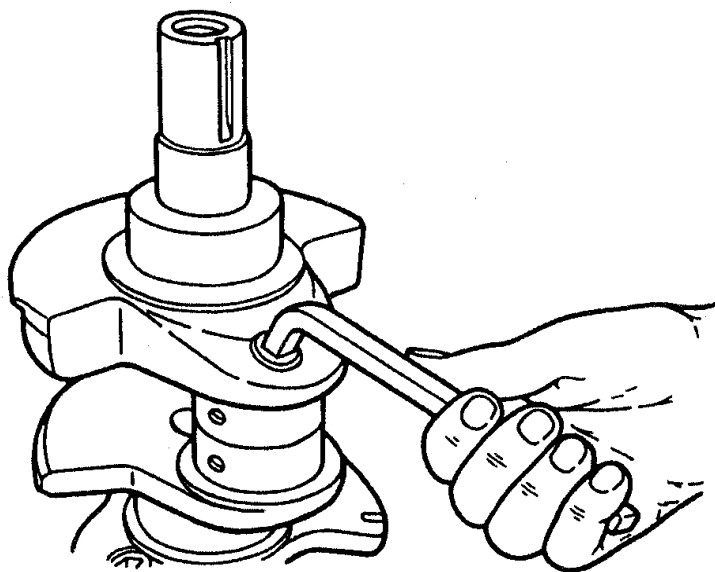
Вывертывание пробок грязеуловителей из коленчатого вала
